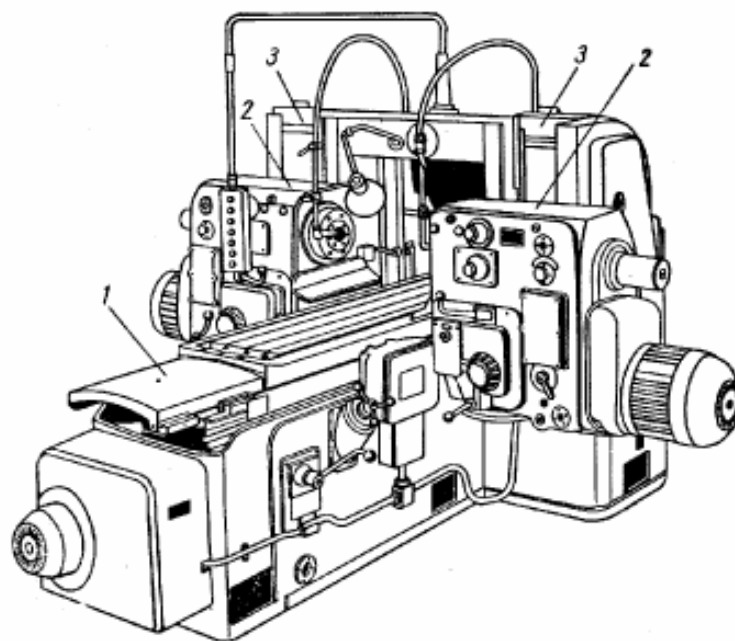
Двухстоечный продольно-фрезерный станок А662
